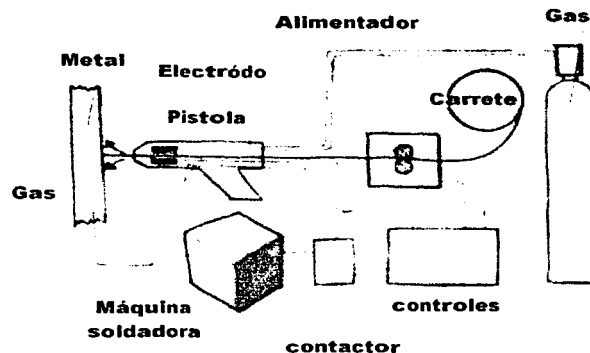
Esquema de un equipo de soldadura MIG
